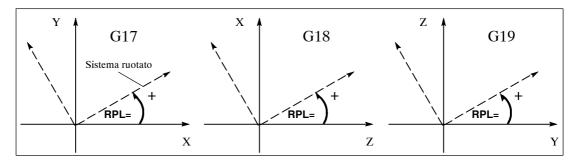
Definizione della direzione positiva dell'angolo di rotazione nei diversi piani
